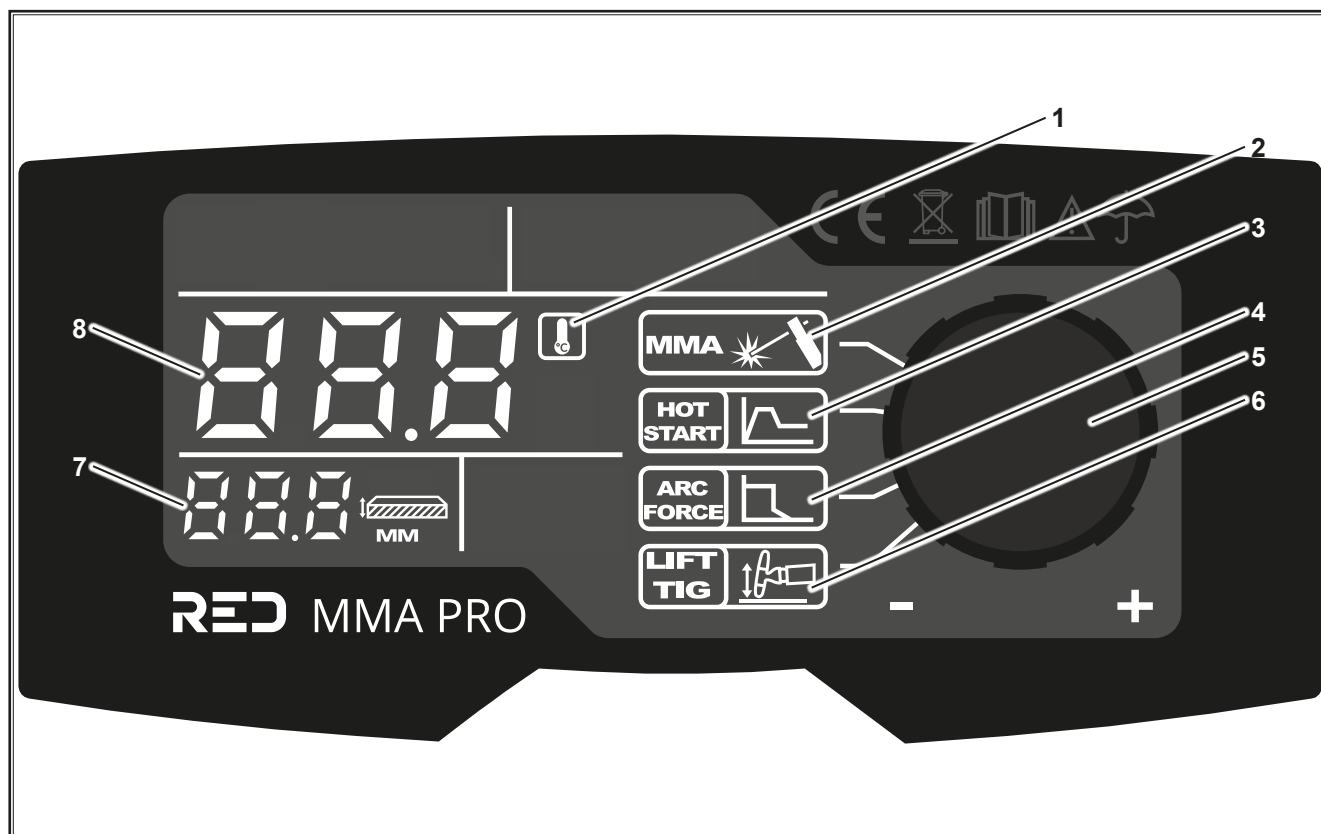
Visualización del proceso de soldadura WIG
